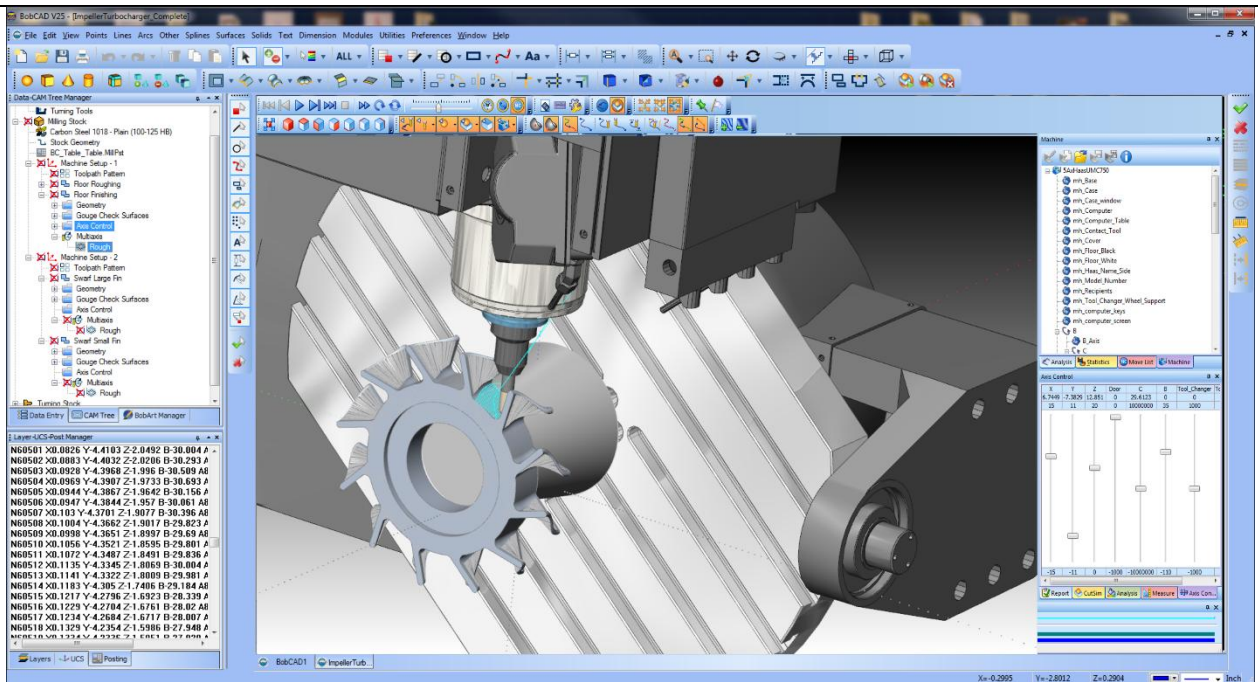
3D CAM Simulyatsiyada Gear Machining
